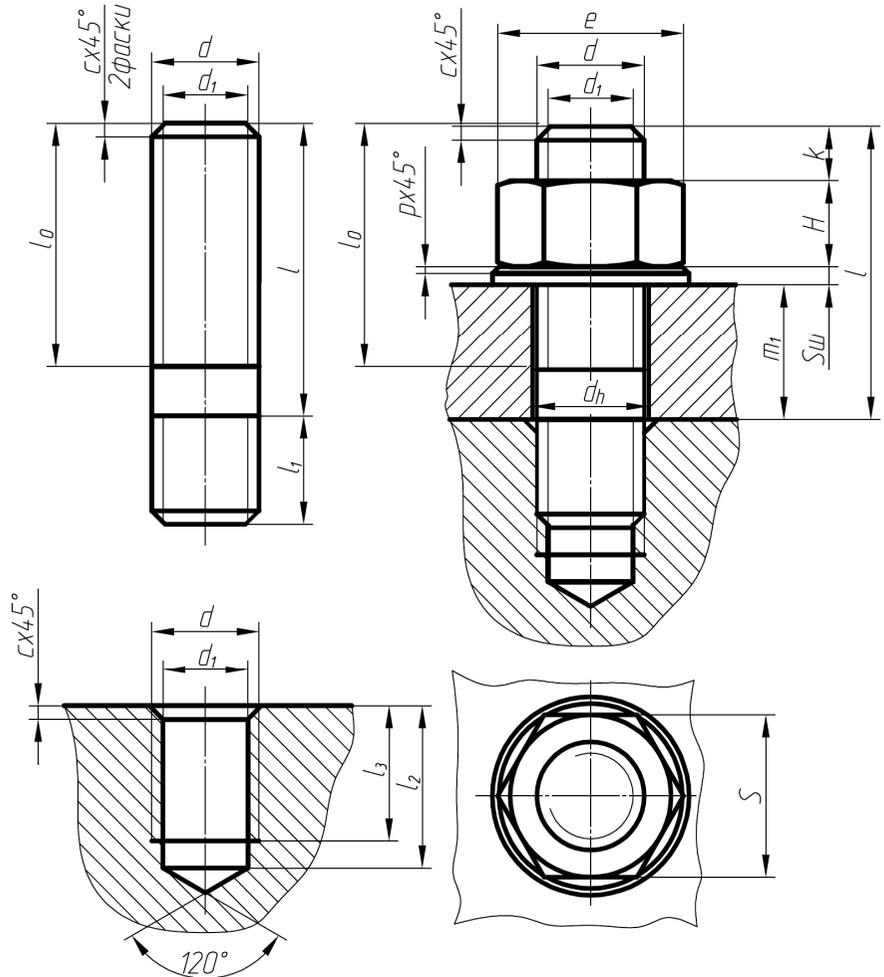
Конструктивные элементы и размеры деталей в соединении шпилькой
